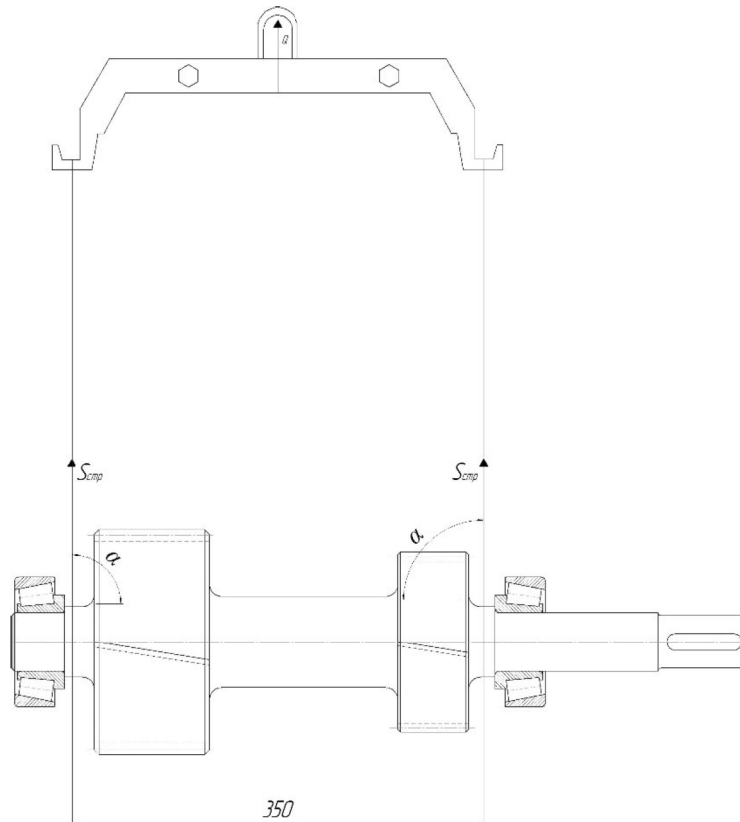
Розрахункова схема швидкохідного редуктора
